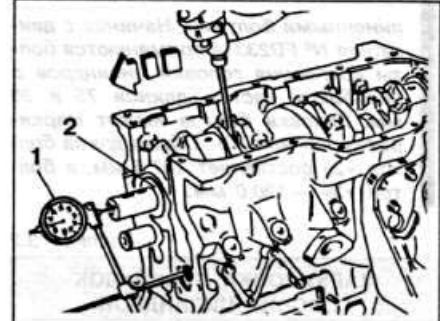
Проверка осевого зазора коленчатого вала:
